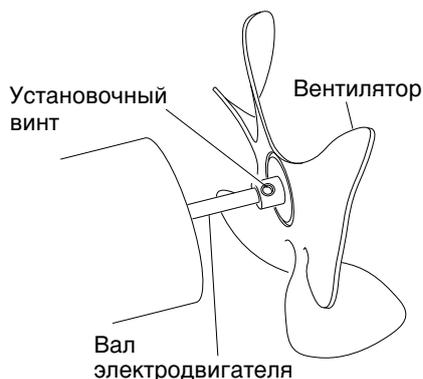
Расположение вентилятора, вала электродвигателя и установочного винта
